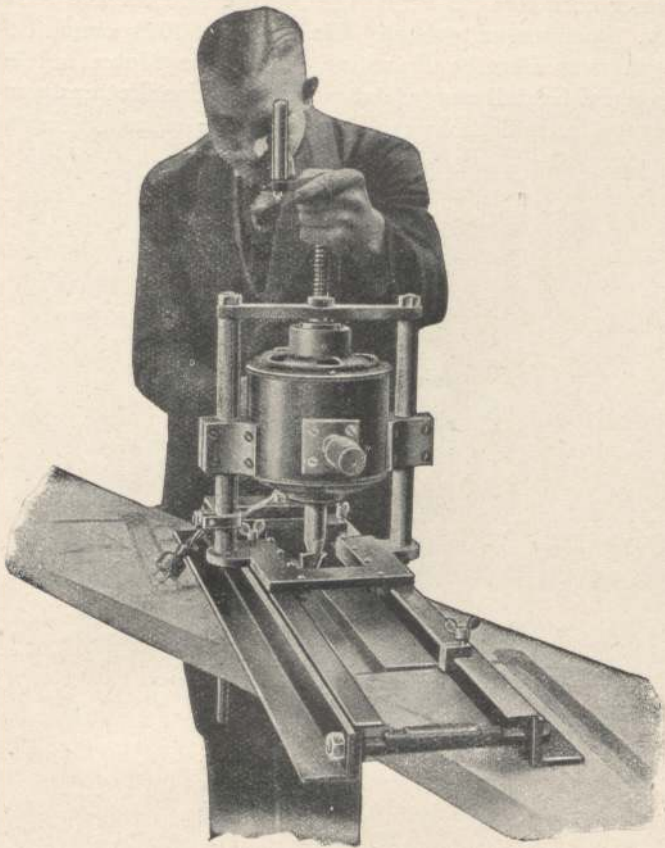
Die transportable „Treppa“-Fräsmaschine.
